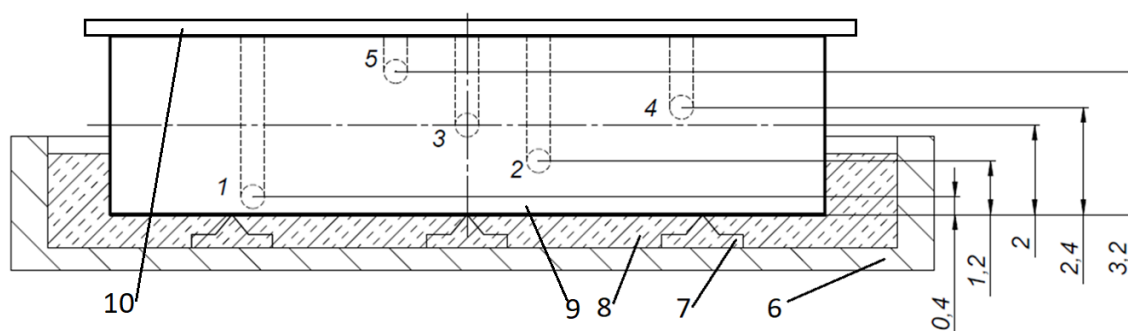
Схема устройства маслonaполнения с указанием координат расположения термодатчиков в образце, где: 1...5 – термодатчики; 6 – ванна; 7 – опоры для создания зазора между образцом и ванной; 8 – масляный наполнитель; 9 – полиамидный образец; 10 – теплоизолятор
